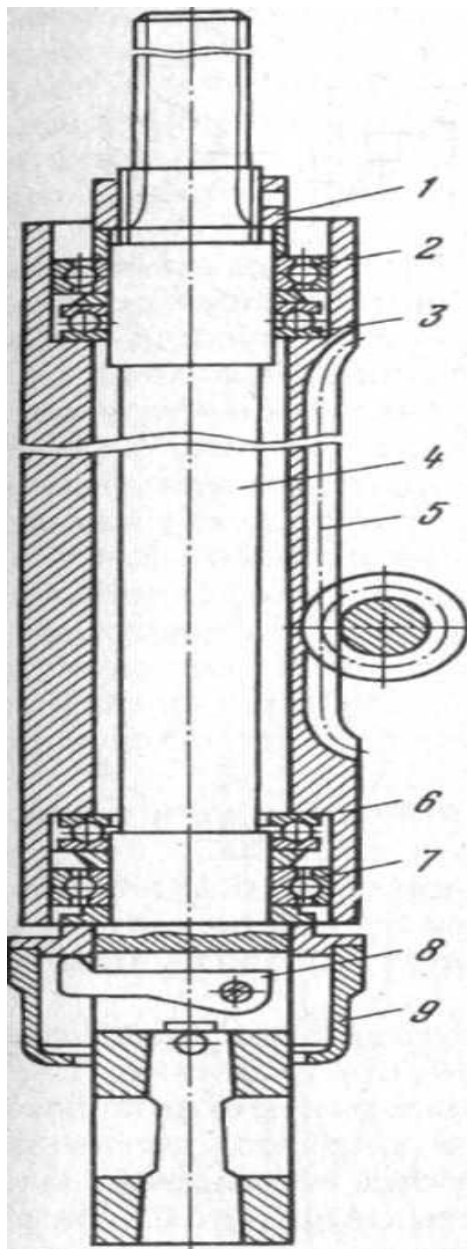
Шпиндельный узел сверлильного станка: 1 – гайка, 2, 7 – радиальные шарикоподшипники. 3, 6 – упорные шарикоподшипники. 4 – шпиндель. 5 – гильза. 8 – рычаг для выталкивания инструмента из шпинделя, 9 – упорный стакан для поворота рычага.
